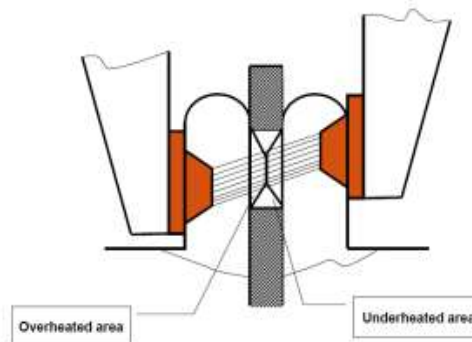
Proyección producida por exceso de energía aportada en la soldadura (Fuente: Material de la empresa).
